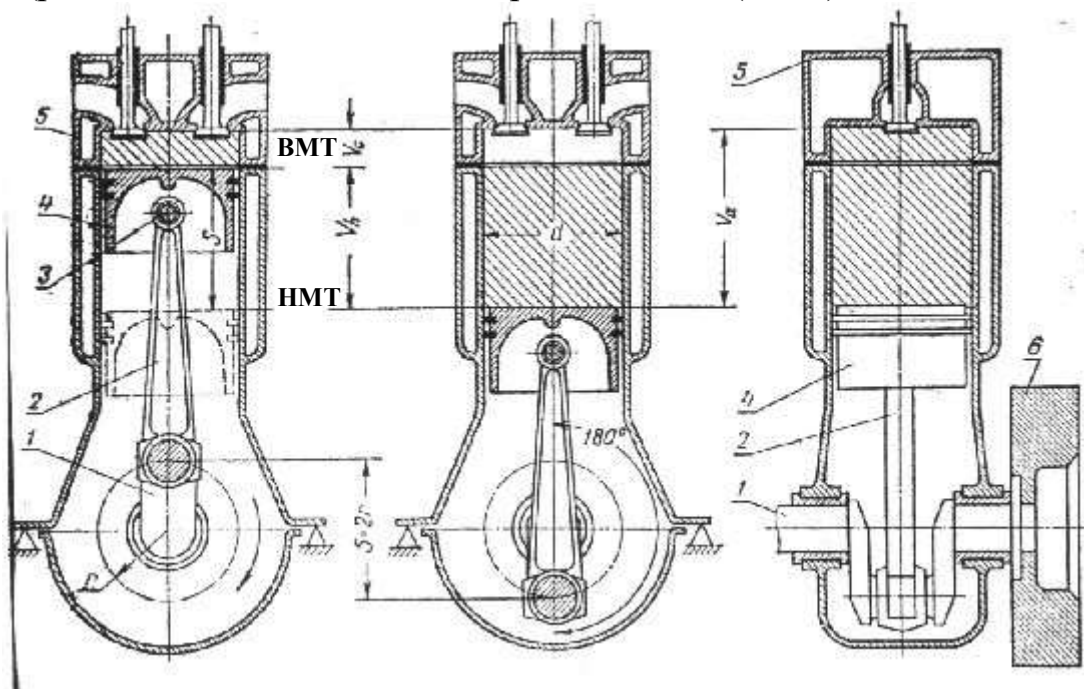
Схема работы кривошипно-шатунного механизма двигателя:
